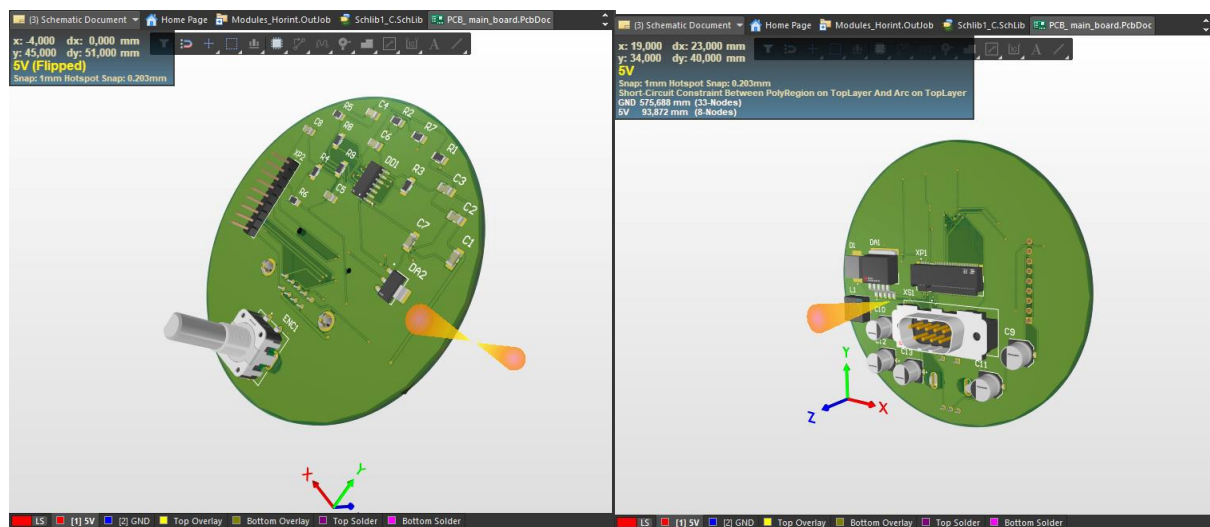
Altium Design ізометричний вид друкованої плати
